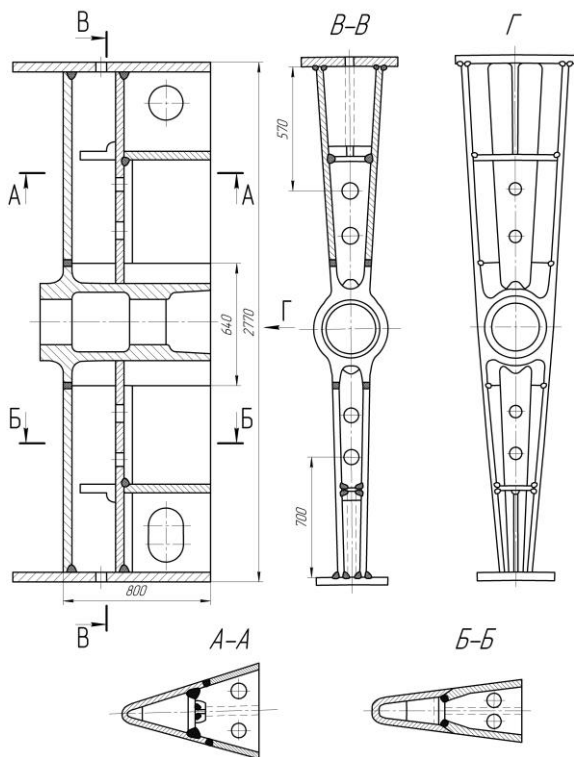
Комбінована зварна конструкція з відливок і прокатних листів
